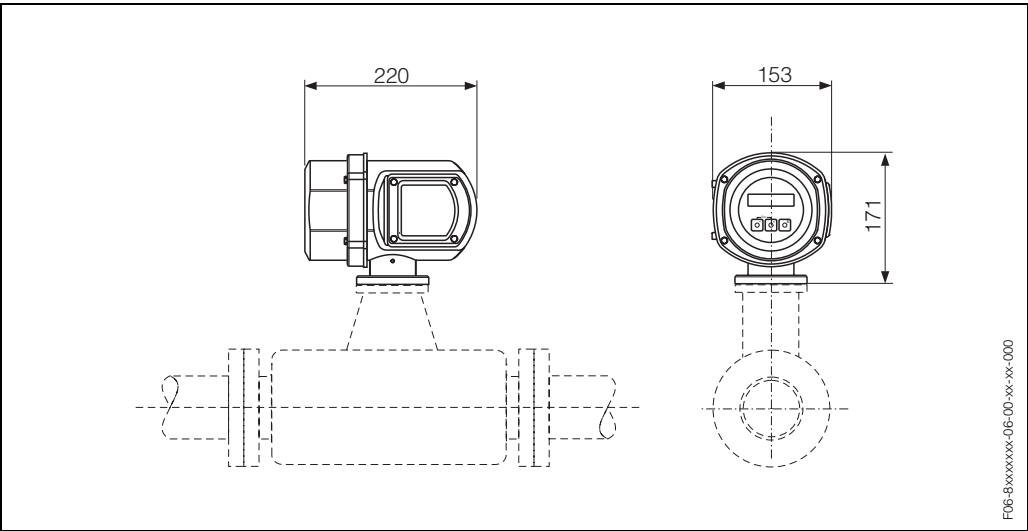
Abmessungen Edelstahl-Feldgehäuse
